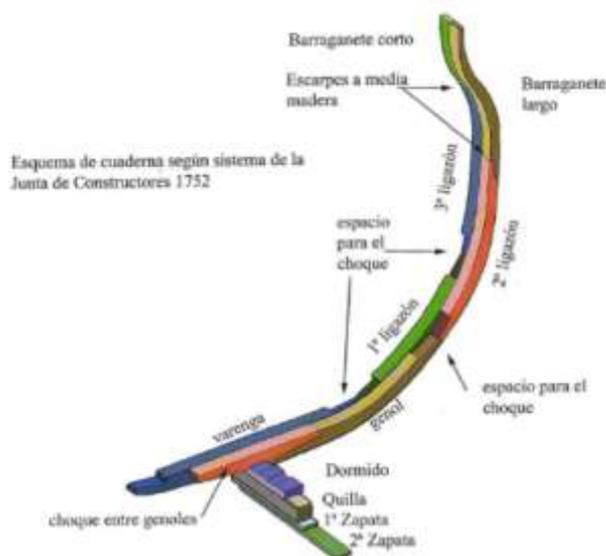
Esquema de la construcción de las cuadernas en el sistema de Jorge Juan en el año 1752
